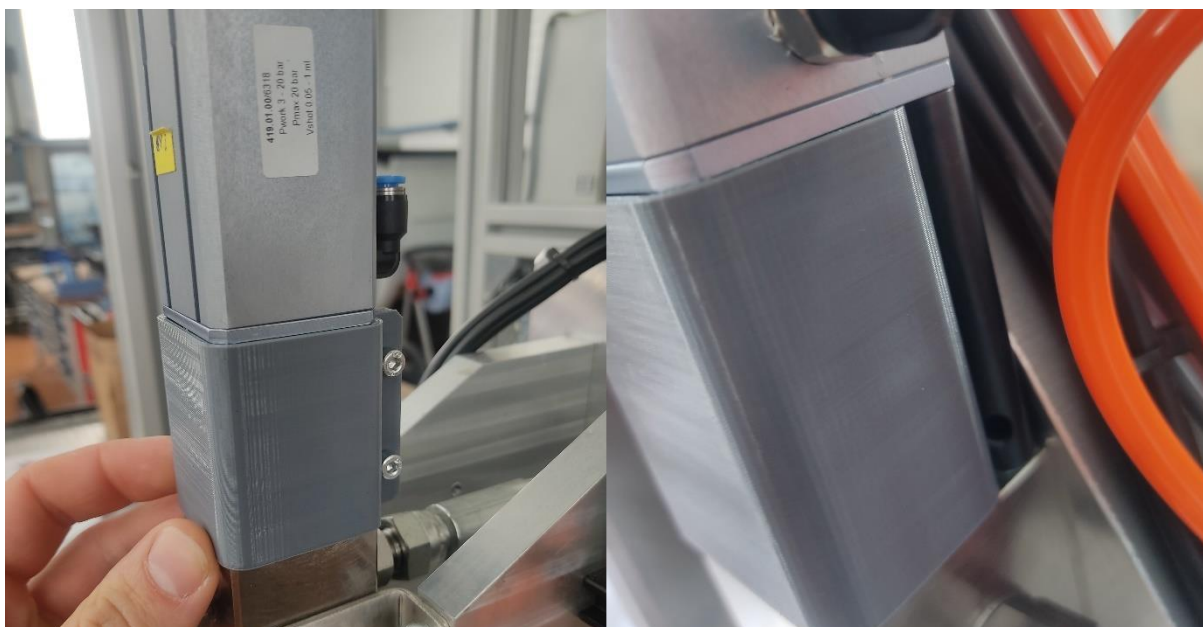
Impressões 3D “*Fused Filament Fabrication*” em PLA cor Cinza
